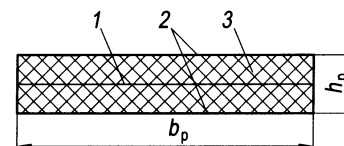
Конструкция кордленточного полиамидного ремня:
